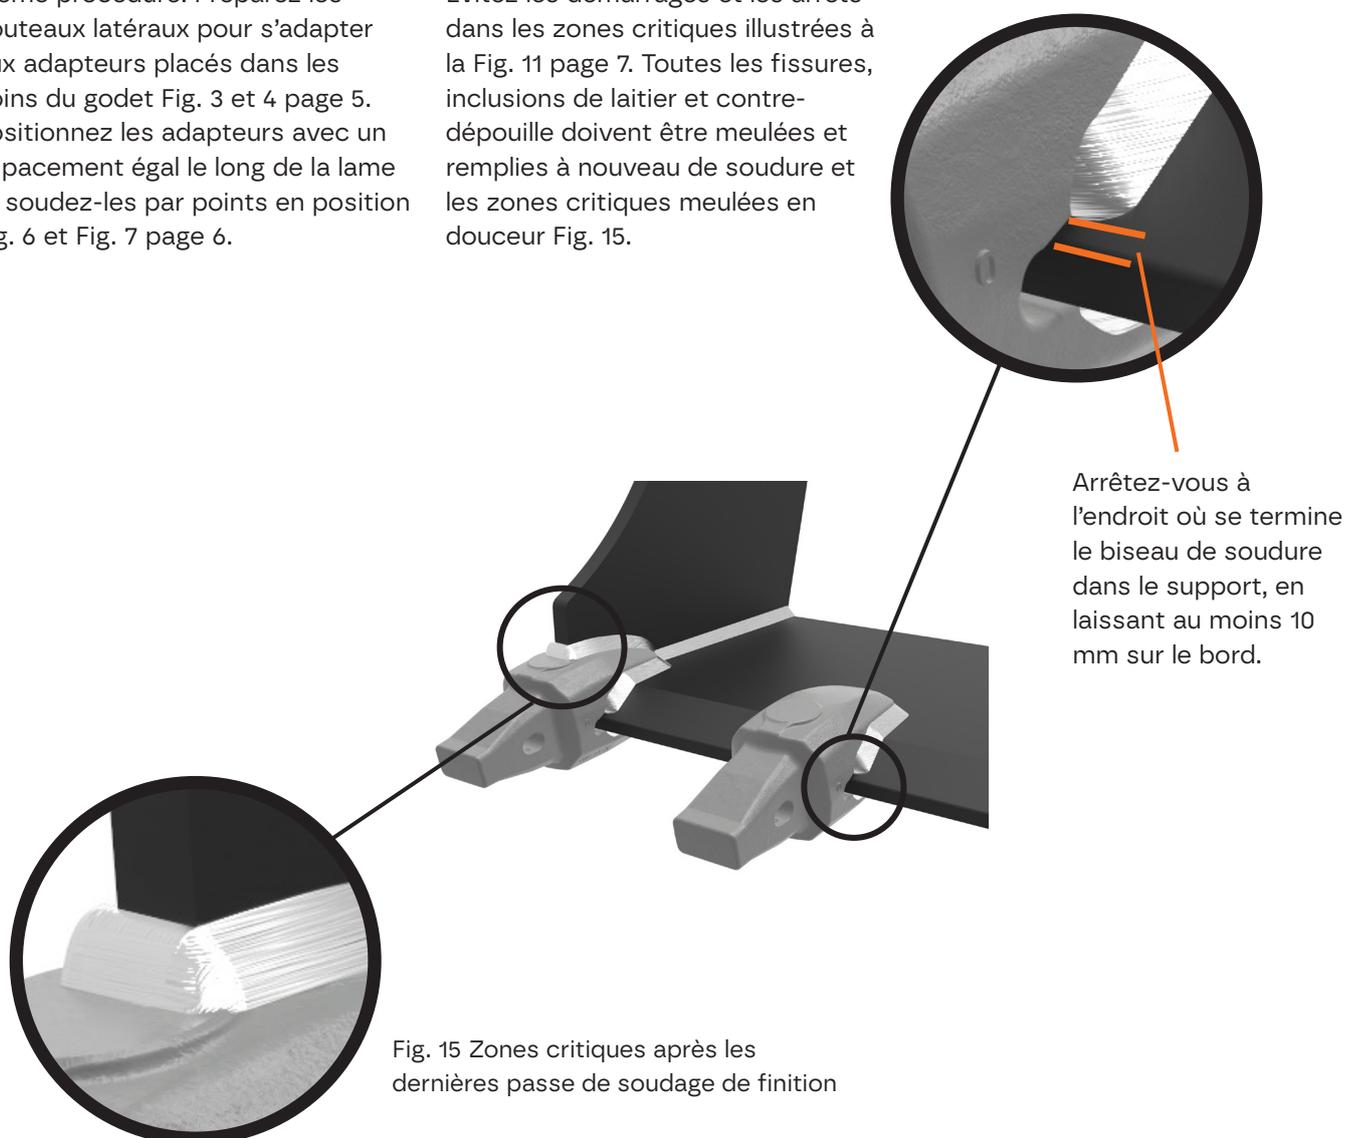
Zones critiques après les dernières passe de soudage de finition
